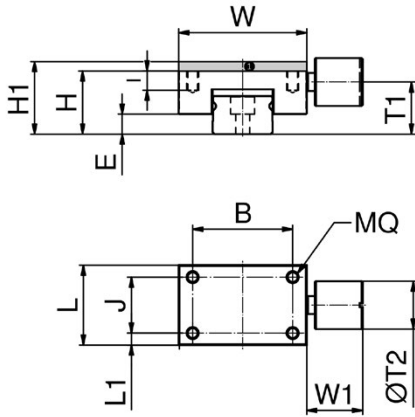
Manuelle Klemmelemente für Miniaturführungen
